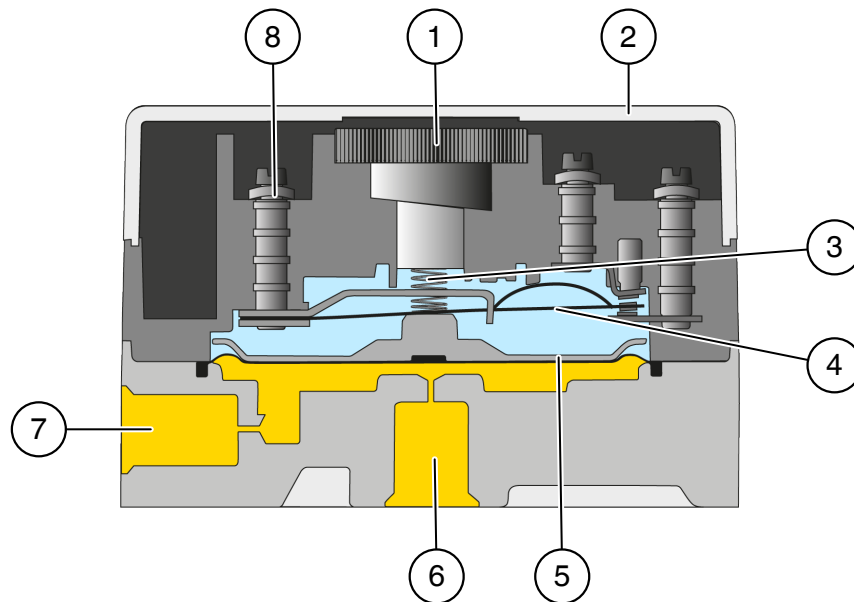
Funktionszeichnung Druckwächter mit einer Druckkammer
